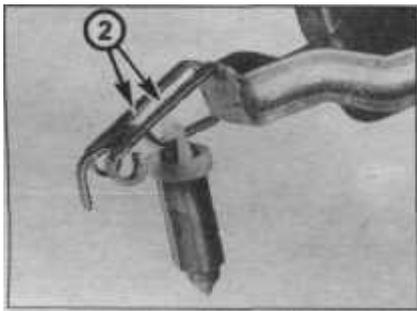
Регулировка верхнего положения поплавка (Глава 19)
